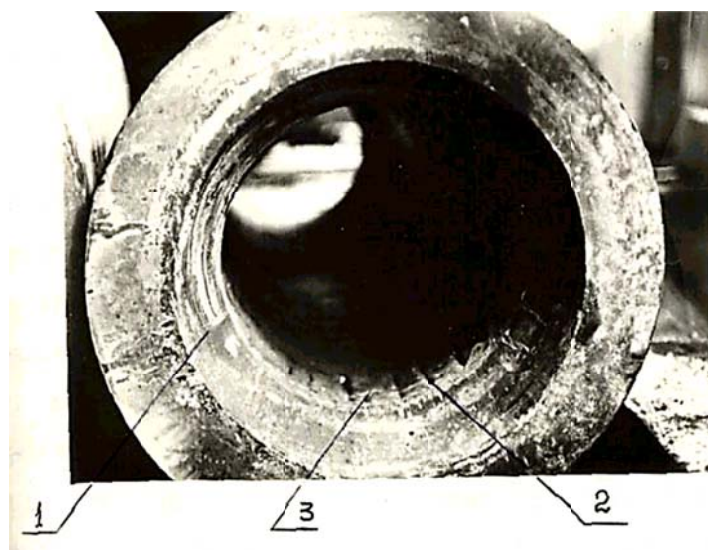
Характерные виды износа рабочей втулки контейнера гидравлического пресса: 1 – истирание металла инструмента; 2 – сетка разгарных трещин; 3 – налипание прессуемого металла
